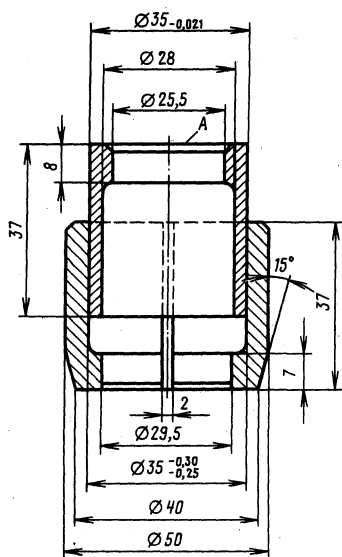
Телескопическая контрольная втулка для измерения расстояния между внутренними кольцами подшипников ведущей шестерни главной передачи автомобиля «Москвич»
